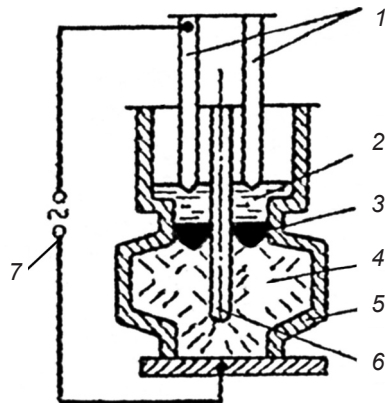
Схема ЭШЛ заготовки корпуса запорной арматуры: 1 – расходные электроды, 2 – шлаковая ванна, 3 – металлическая ванна, 4 – заготовка, 5 – кристаллизатор, 6 – дорн, 7 – источник тока
